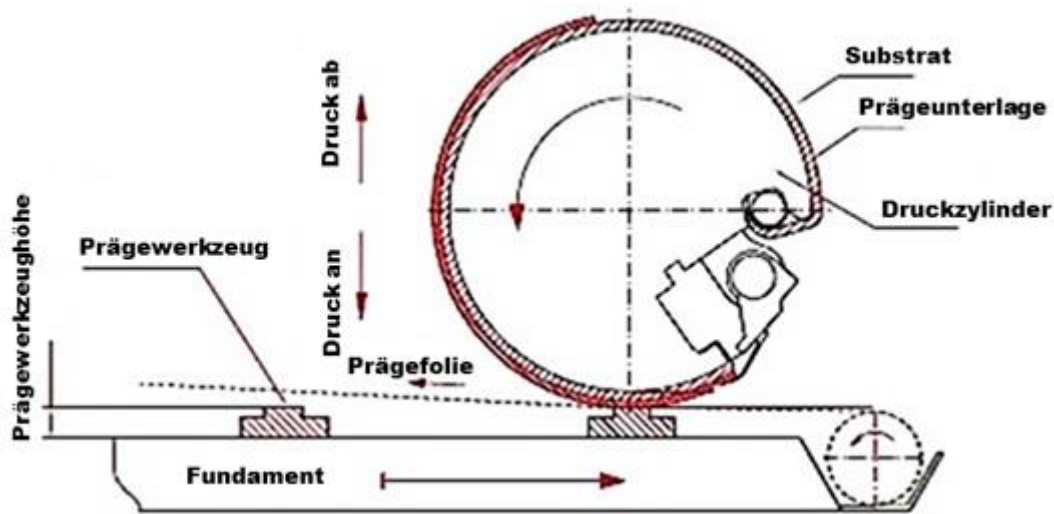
Skizze einer Prägefoliendruckmaschine „Rund auf Flach“. Das Prägewerkzeug ist flach, die Gegendruckform mit dem Druckzylinder ist rund. Bildquelle: [ARB05].
